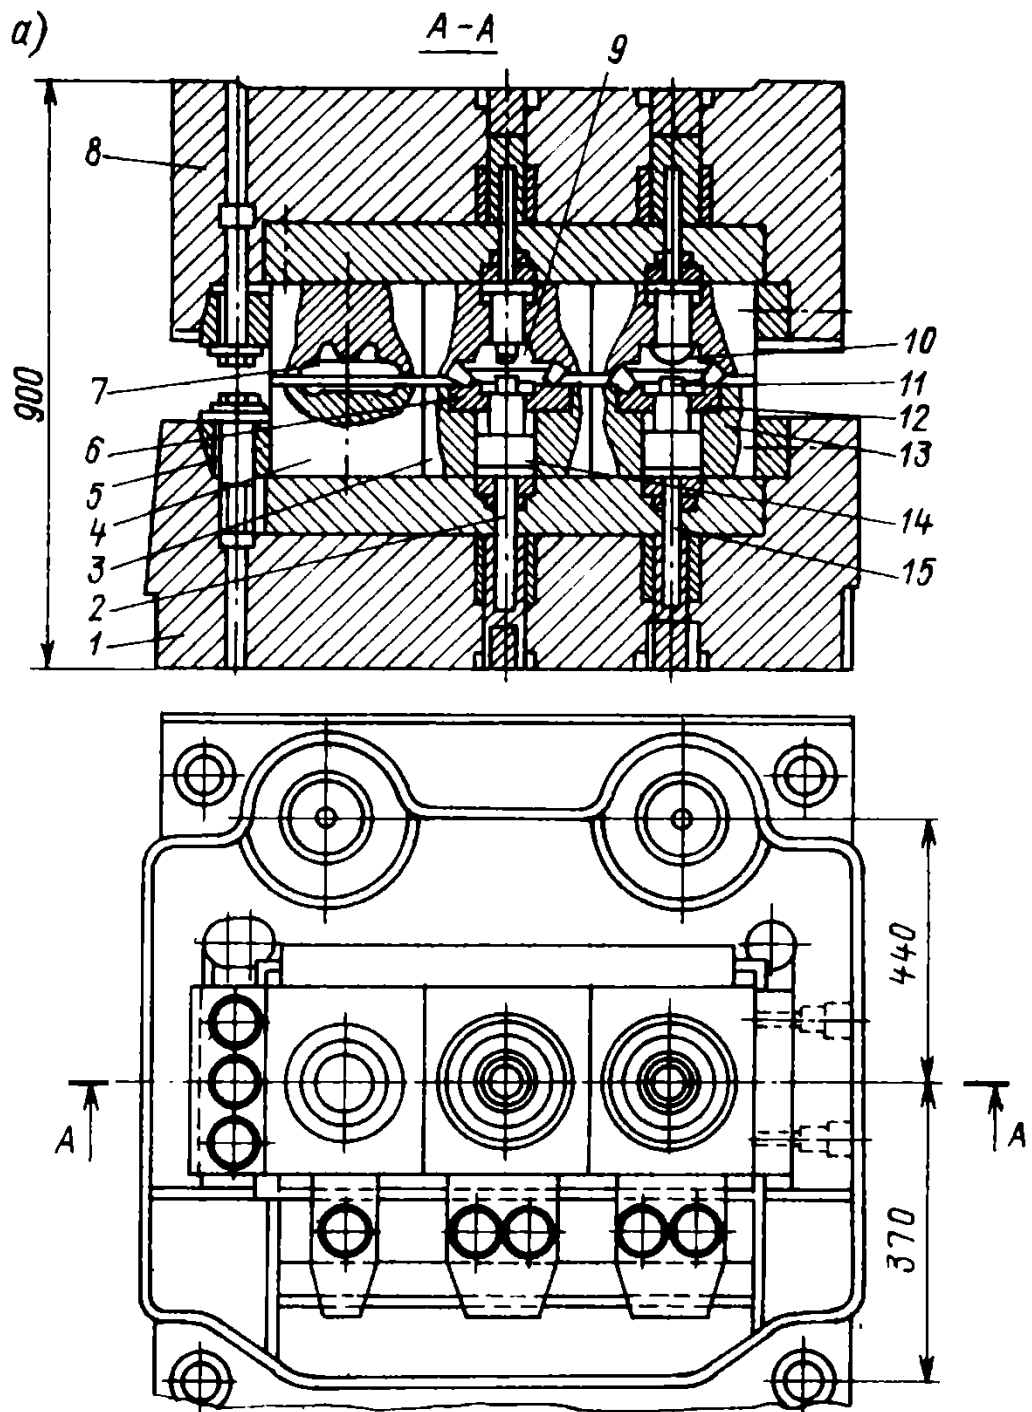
Штамп для штамповки поковки шестерни с зубом
